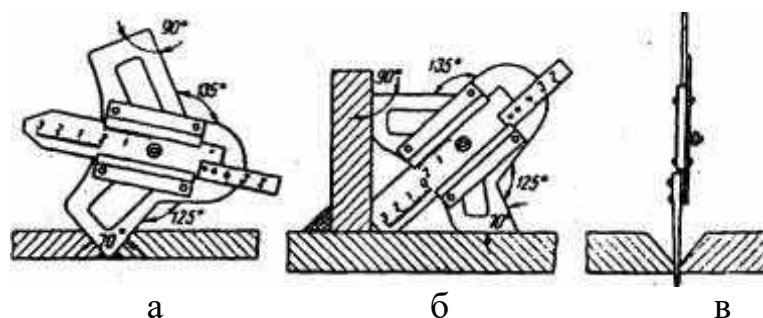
Примеры применения универсального шаблона конструкции инж. Ушера-Маршака: а – проверка угла разделки; б – проверка перпендикулярности деталей; в – контроль зазора в стыковом соединении
